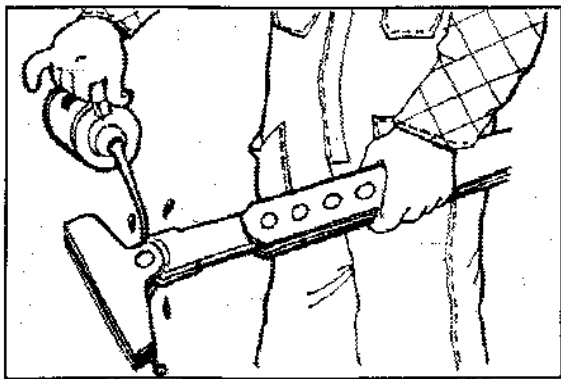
Схема смазки шарнирных узлов крепежных приспособлений.
